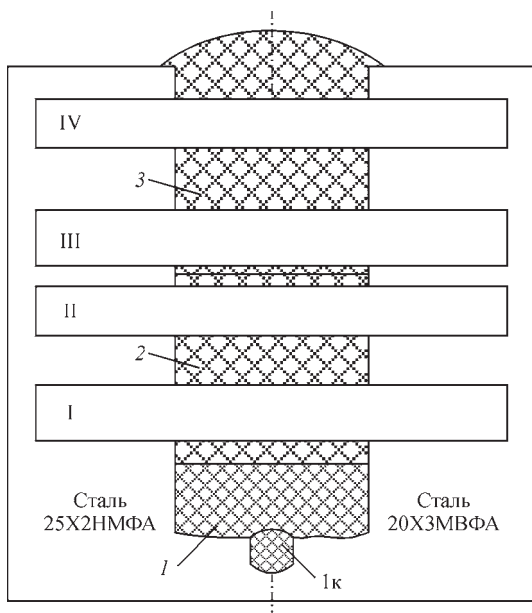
Схема вирізки з комбінованого зварного з'єднання зразків I–IV для вивчення структури I–3 зони зварного з'єднання: I – коренева; 2 – середня; 3 – верхня; Iк – нижня ділянка кореневої зони I
